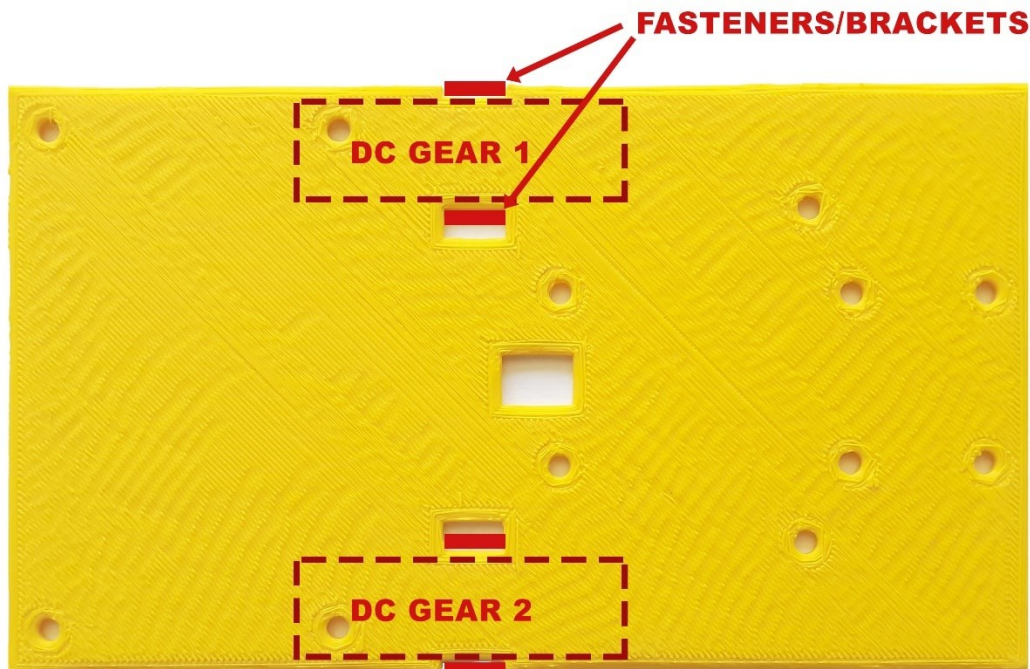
Imagem de 2: Diagrama da colocação dos 2 motores (engrenagem DC) e dos 4 suportes (fixadores/suportes)
